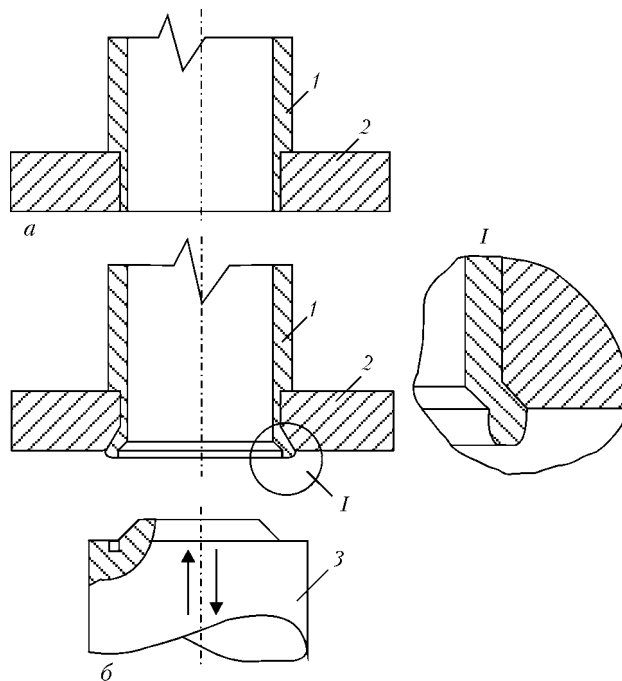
Схемы жесткого фланцевого соединения (а) и его сваркопайки с отбортовкой трубы по внутренней поверхности фланца (б): 1 – труба; 2 – фланец; 3 – сварочный пуансон
